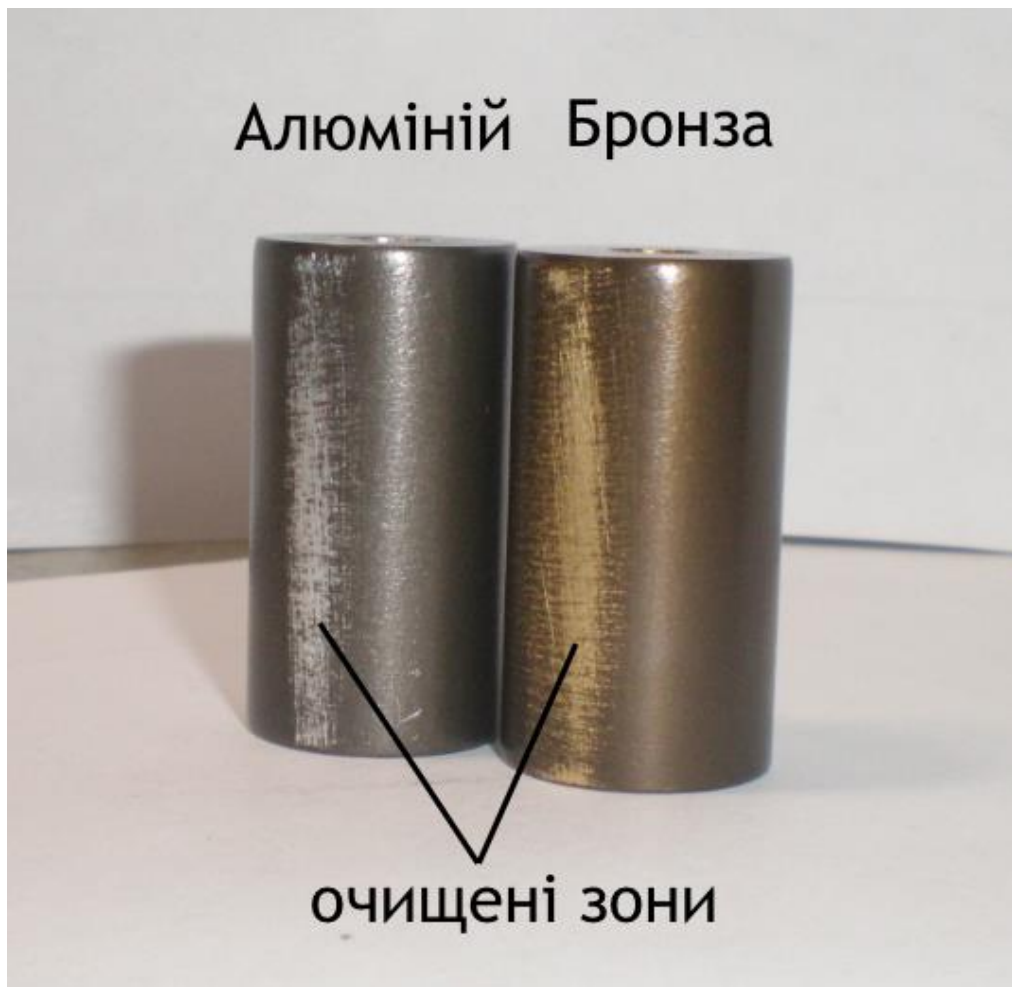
Поверхневий шар зразків після оброблення
